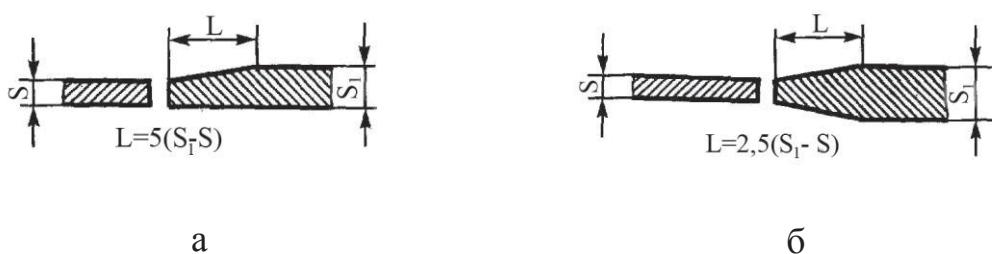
Разделка кромок под сварку листов разной толщины:
